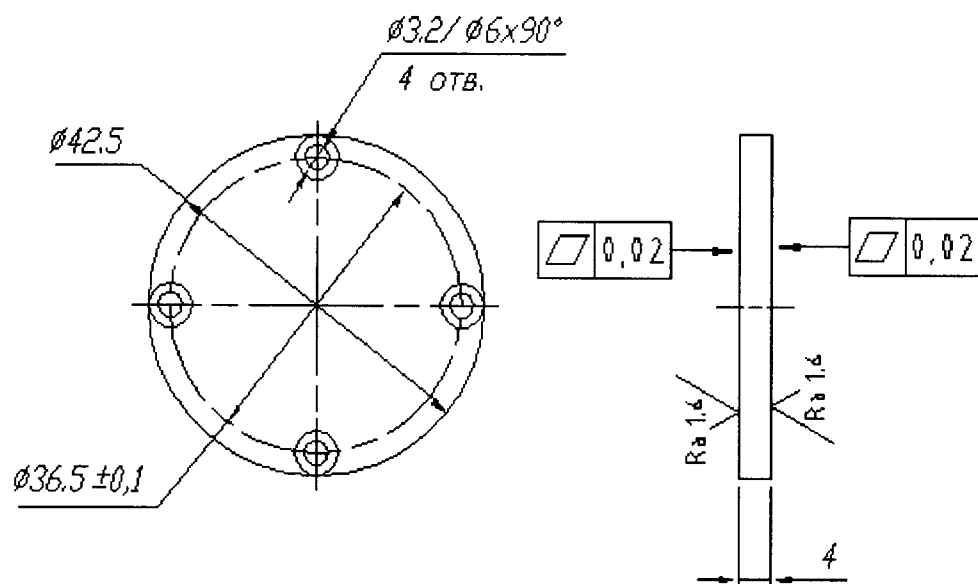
Конструкция образца металла для установки в юстировочное устройство
